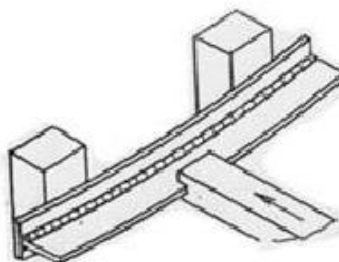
Схема исправления сварной тавровой балки путем приложения статической нагрузки
